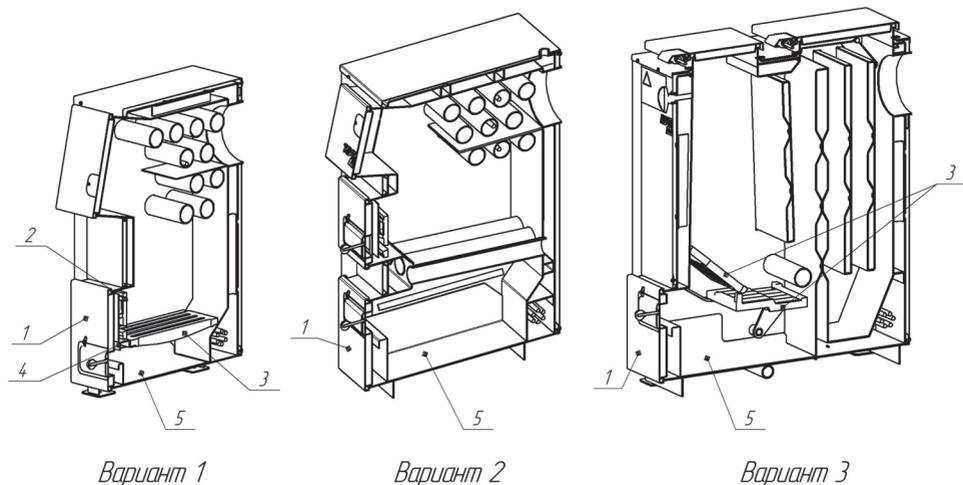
Подготовка печи к установке газогорелочного устройства
